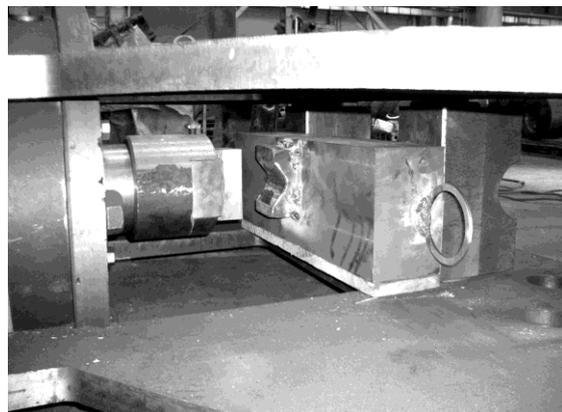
Трубогиб оснащённый для заковки конца заготовки
